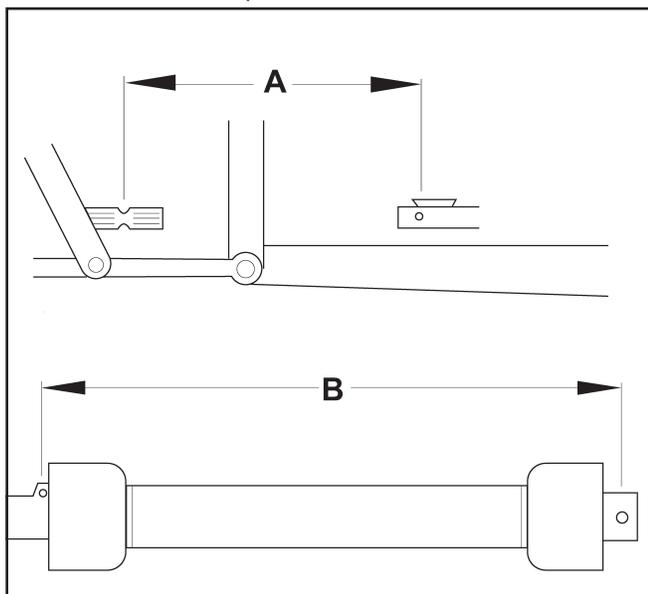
Dimensions de l'équipement (A) et dimension de l'arbre de transmission non coupé (B).
